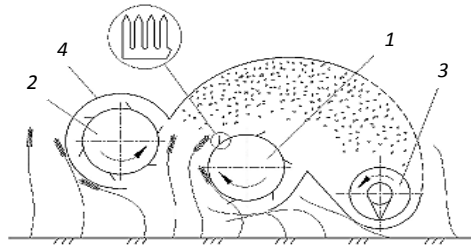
Схема двухбарабанной жатки очесывающего типа: 1– барабан очесывающий; 2 – битер-отражатель; 3 – шнековый транспортер; 4 – передний кожух
